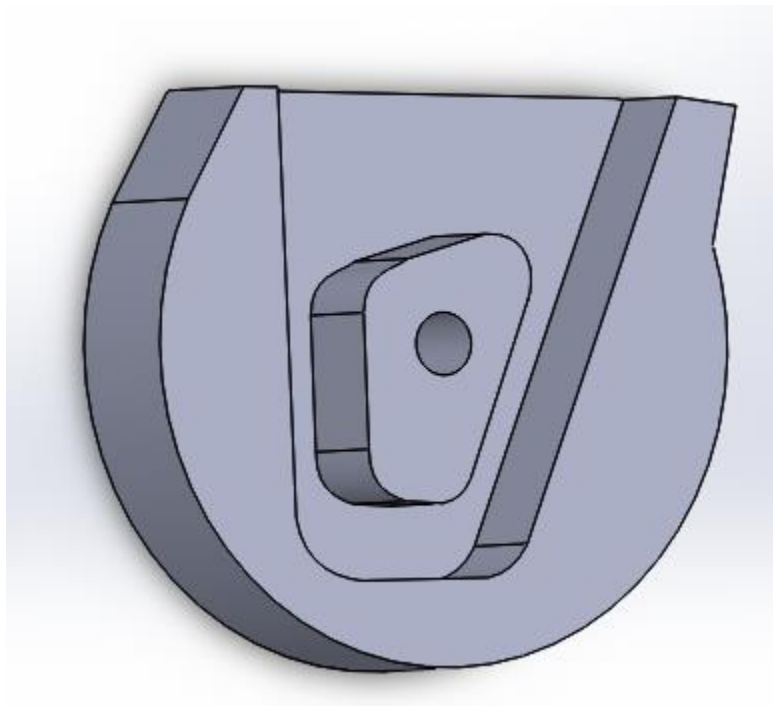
Diseño del soporte fijo Version 1. Fuente: Autor.
